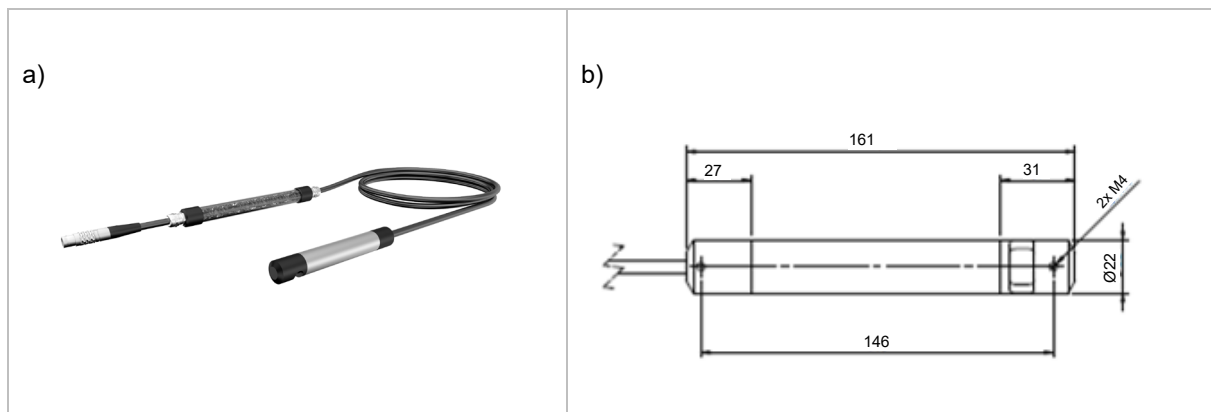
a) Drucksensor mit Trockenpatrone, b) Abmessungen Drucksensor in mm
